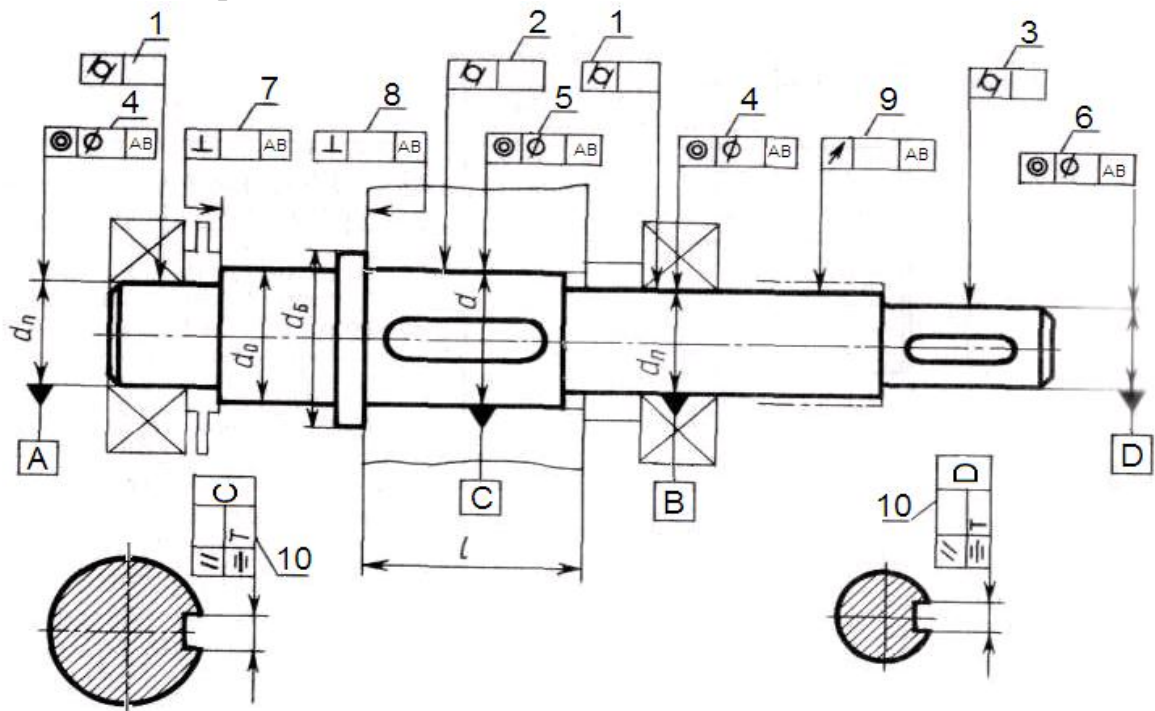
Позначення допусків форми і розташування поверхонь вала на кресленнях
